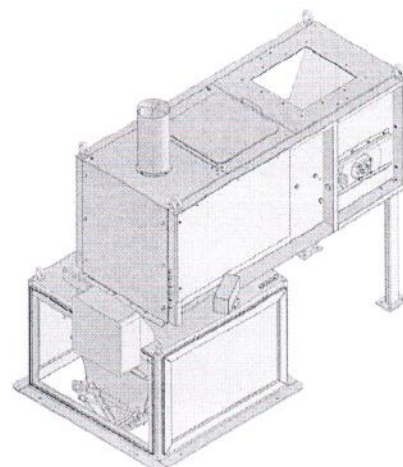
Внешний вид весов с защитным кожухом и ленточным питателем
